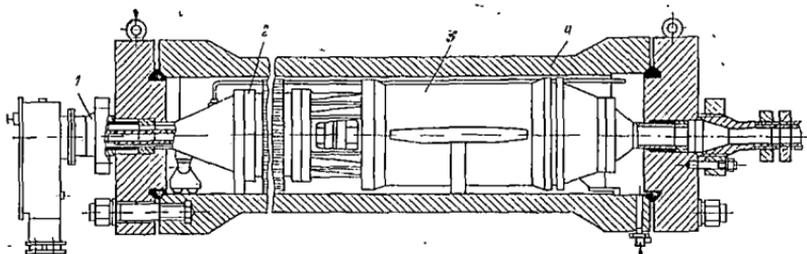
Компрессор типа ЦЦК с вертикальным разъемом корпуса
